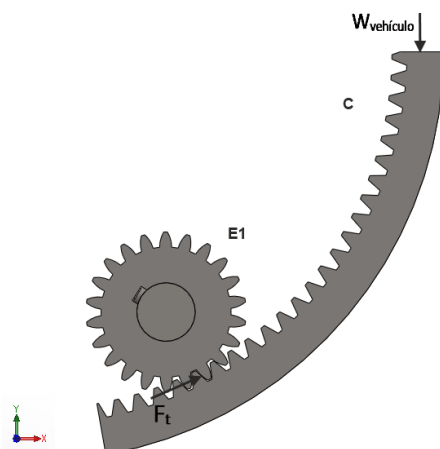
Fuerzas actuantes en el engranaje E1 y corona. Fuente: Elaboración propia.
